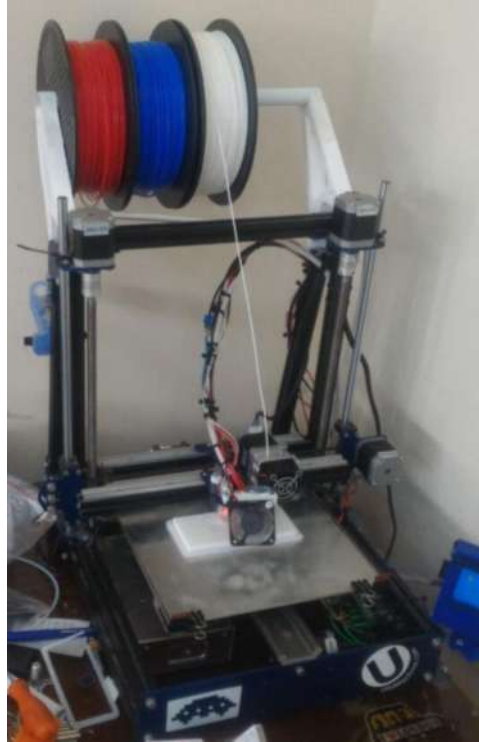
Impresora 3d Ultimachine Mendelmax2.
